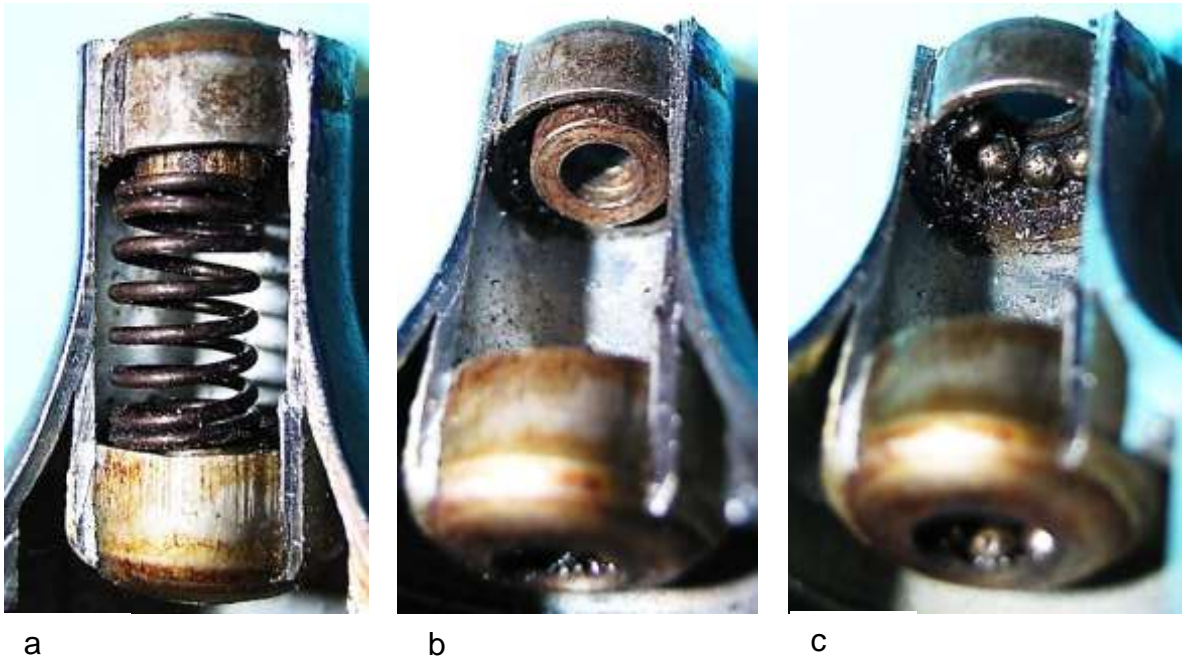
Kugellager: a) Vollständiges Lager, b) Schraubenfeder entfernt mit Blick auf den oberen Konus, c) Obere Lagerschale mit Kugeln
